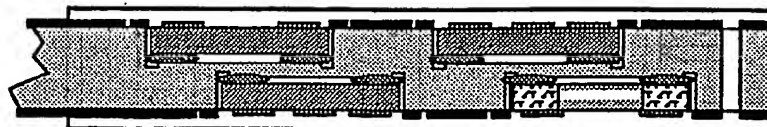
Bohrungen und ausgefräste Mikrochip-Senken (hier für beidseitige Bestückung)
